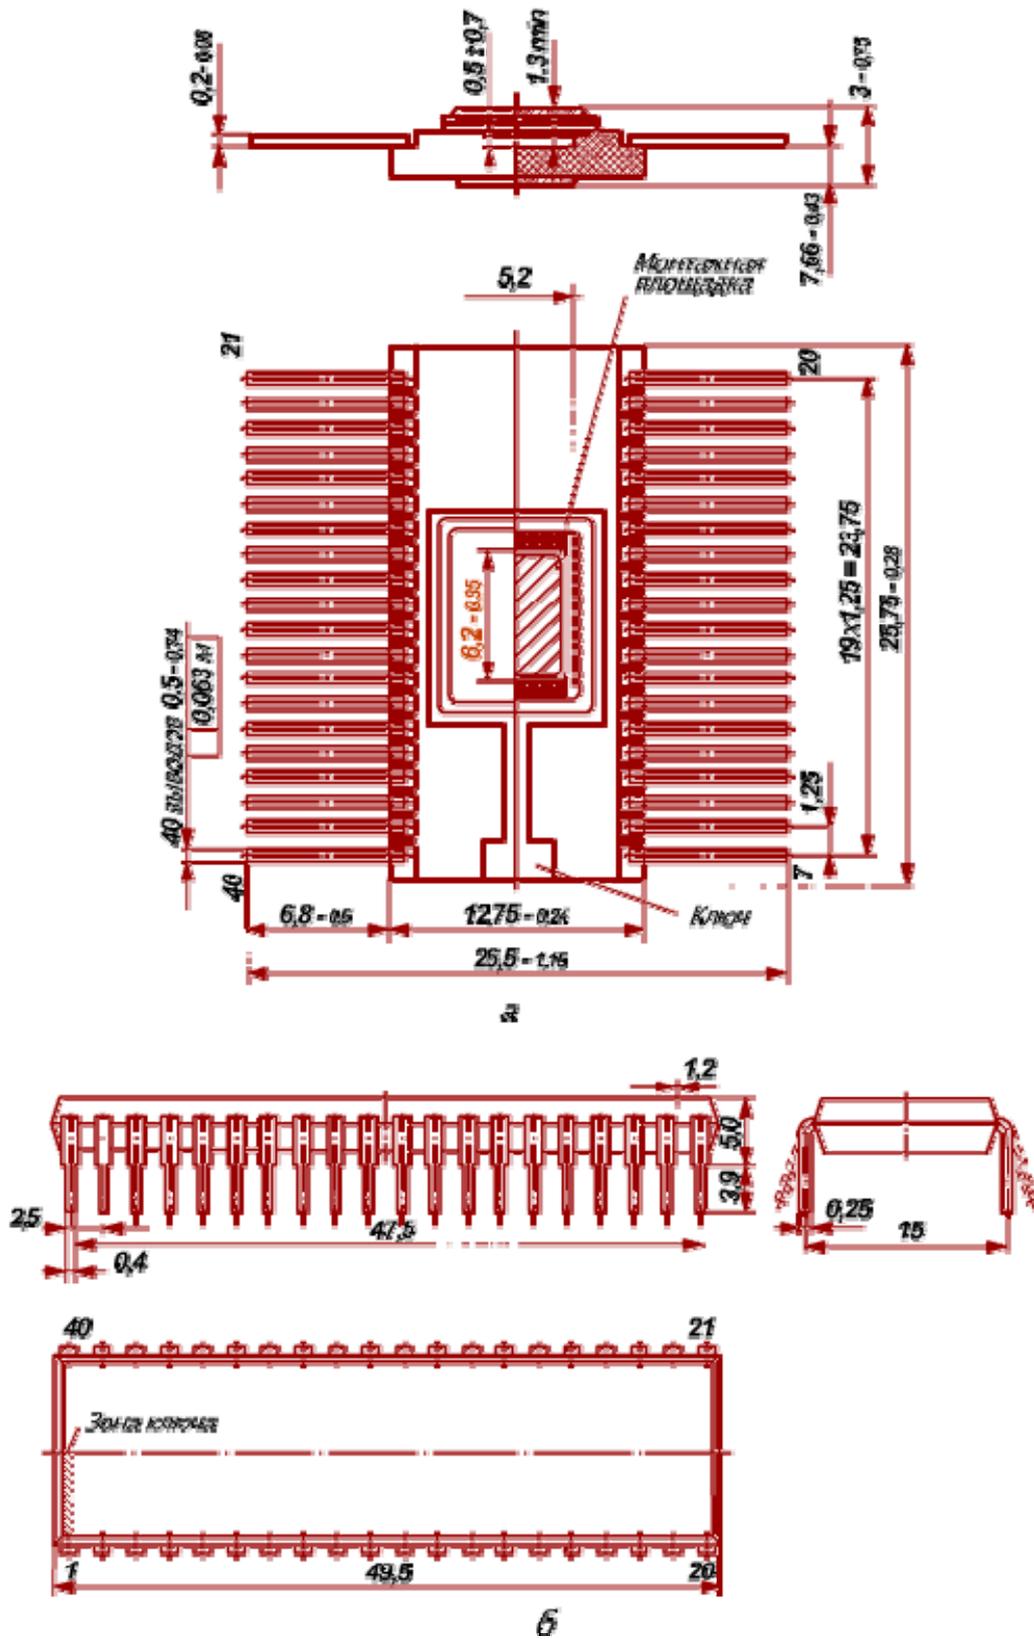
Конструкция металлокерамического корпуса (а) и пластмассового корпуса (б)
